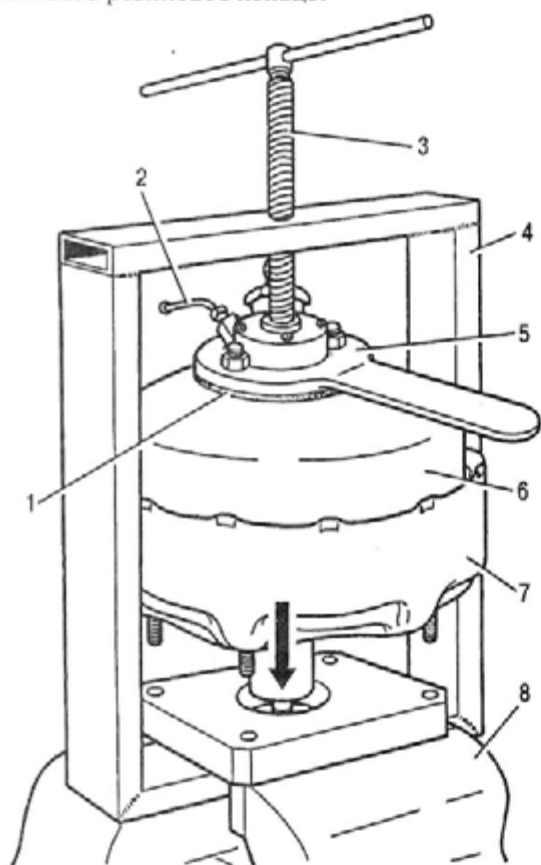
Приспособление для разборки и сборки усилителя: 1 - прокладка; 2 - вакуумная трубка; 3 - упорный винт; 4 - приспособление; 5 - ключ-заглушка; 6 - крышка вакуумного усилителя; 7 - корпус вакуумного усилителя; 8 - тиски
